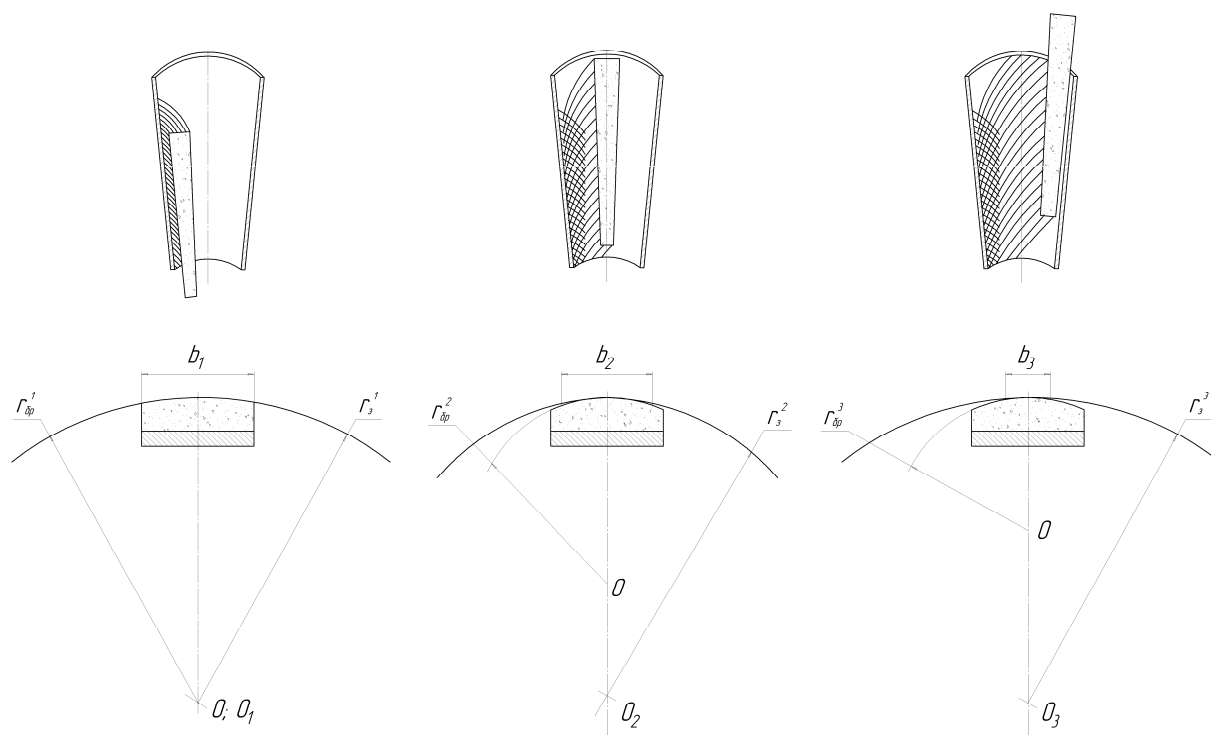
Схема изменения ширины контакта рабочей поверхности інструмента с деталлю
